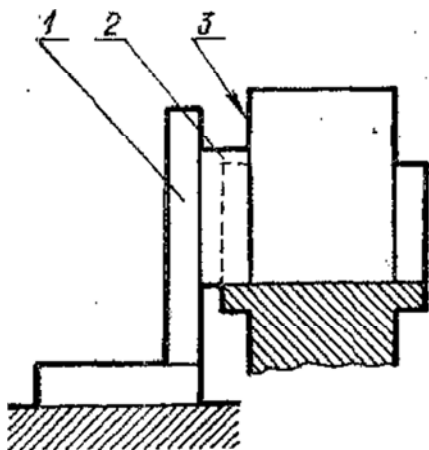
Выверка заготовки в тисках при фрезеровании горизонтально расположенных торцов прямоугольного бруска
